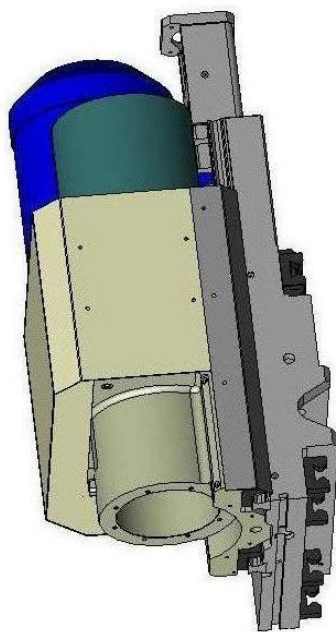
3D конструкція супорта верстата в зборі шпиндельною бабкою
